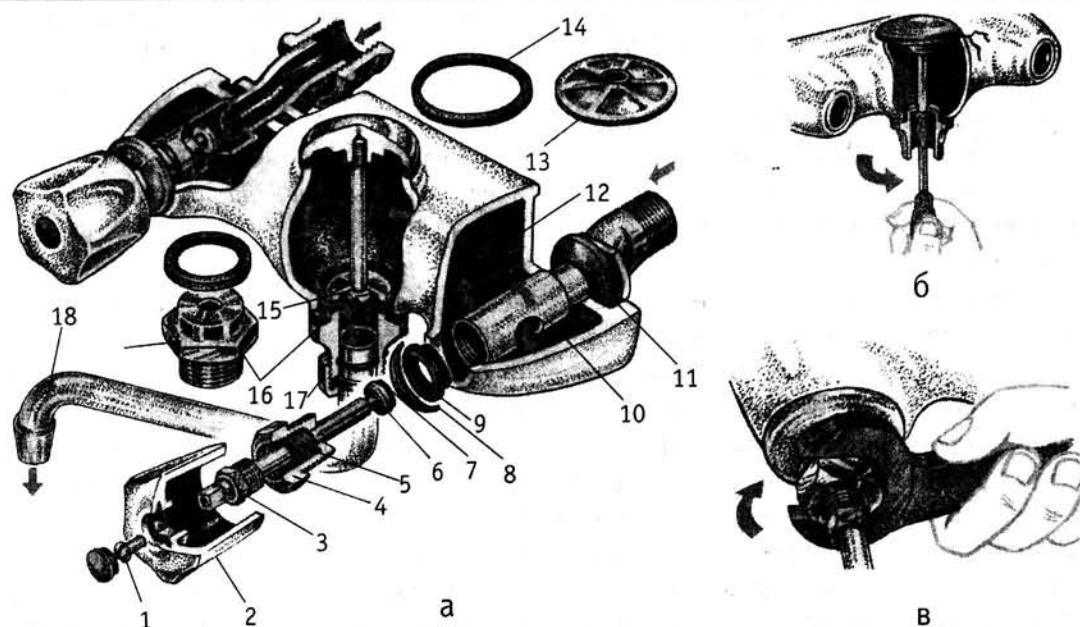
Смеситель настенный с нижним изливом и фарфоровым корпусом для умывальников типа См-УмНВФА
